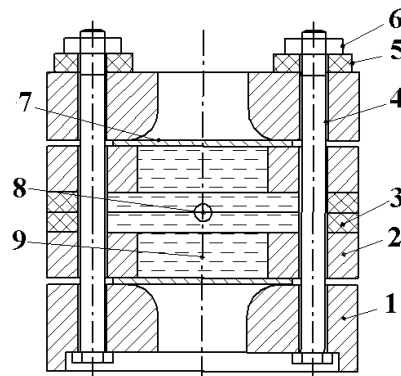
Схема нового устройства для штамповки листовых деталей:
